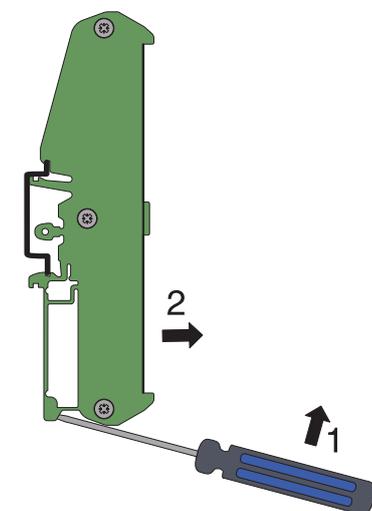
Демонтаж барьеров ЭНИ-БИС-112...116, 118-Ех-DIN с DIN-рейки
